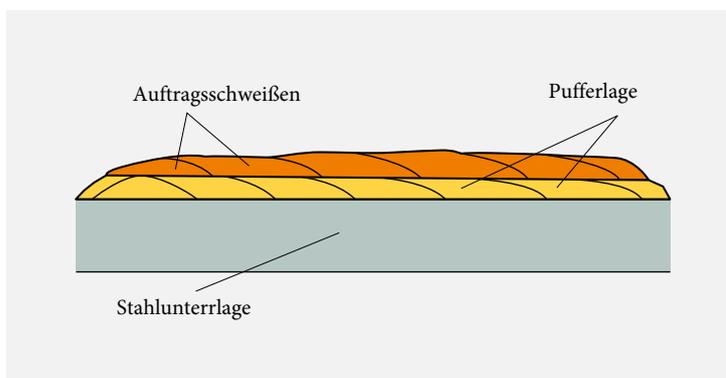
Beispiel einer Schweißsequenz unter Verwendung von Zusatzwerkstoffen für Pufferlage und Auftragsschweißen
